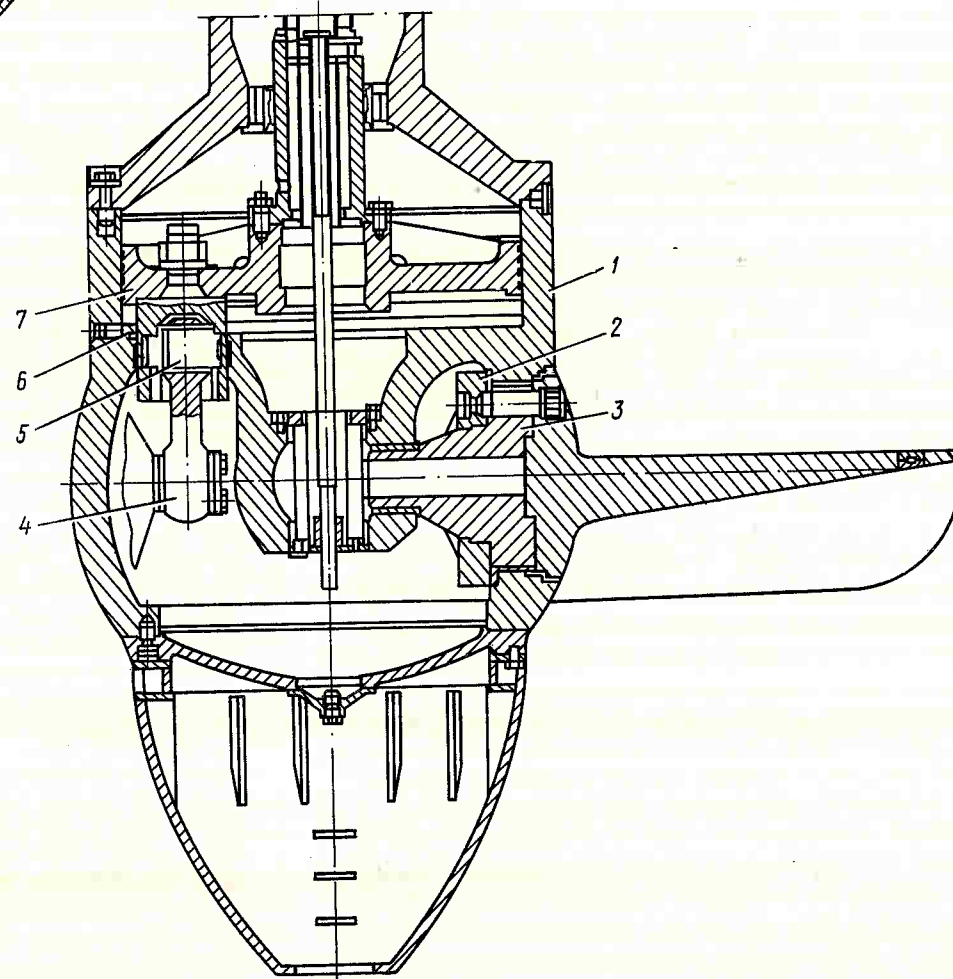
Разрез по рабочему колесу бескрестовинного типа поворотной-лопастной гидротурбины:
